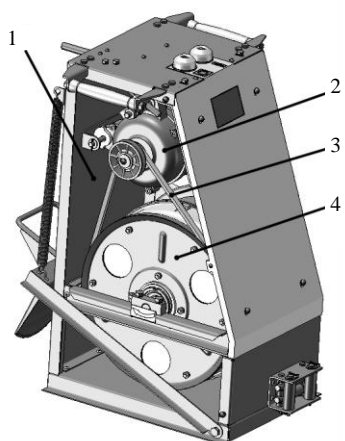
Общий вид лебедки сельскохозяйственной ЛС-100А со снятой крышкой:
